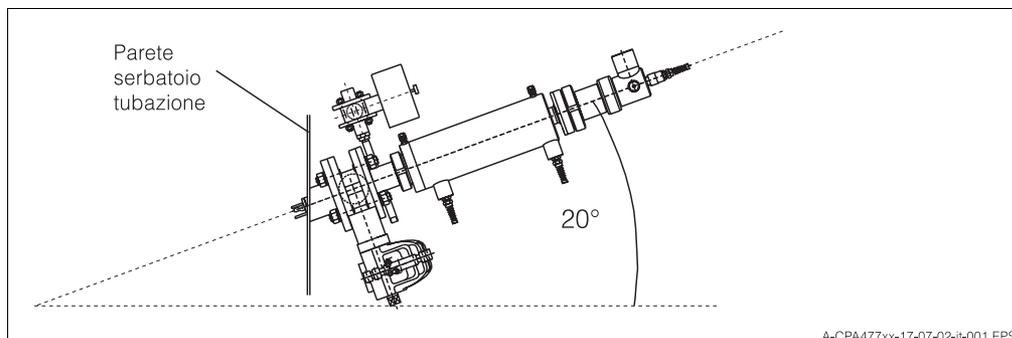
Montaggio del CPA 477. L'angolo d'installazione dovrebbe essere di 20° rispetto al piano orizzontale.
